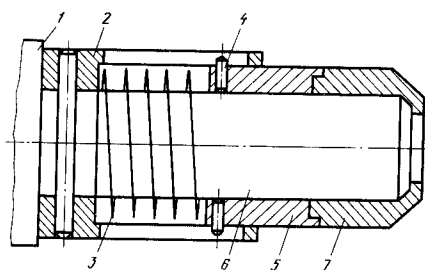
Приспособление для полной фиксации положения заготовки на оправке: 1, 5 — втулки; 2, 4 — штифты; 3 — пружина; 6 — оправка; 7 — заготовка
